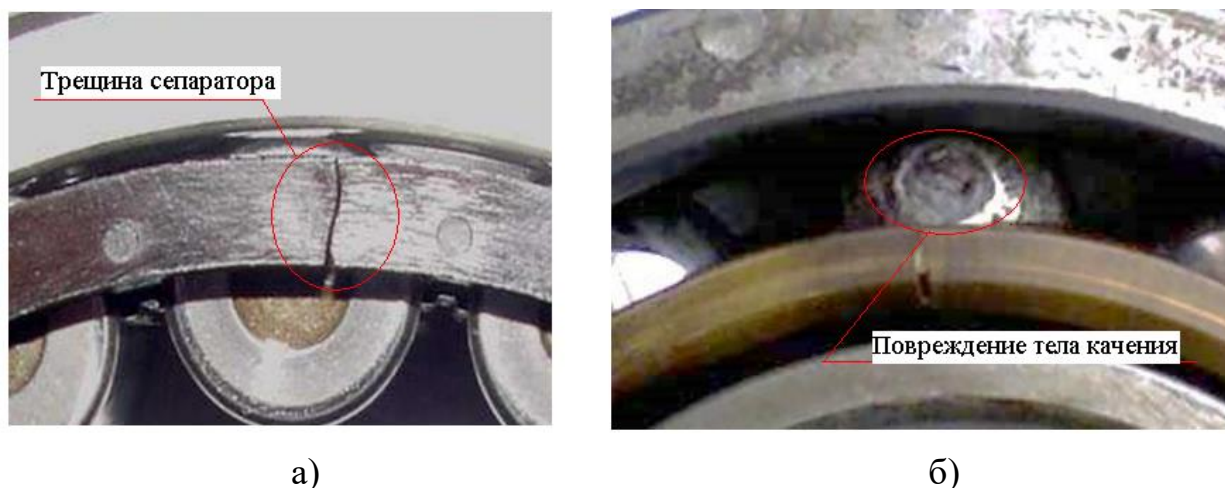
Осмотр подшипника: а) трещина сепаратора; б) повреждение тела качения
